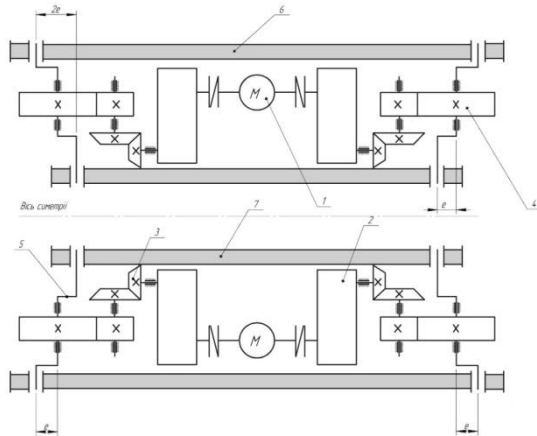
Кінематична схема моделі крокуючого чотирьохопорного механізму: 1– електродвигун із двома вихідними валами; 2– редуктори; 3– конічні передачі; 4– відкриті зубчасті передачі; 5 – вали; 6, 7 – опорні башмаки
